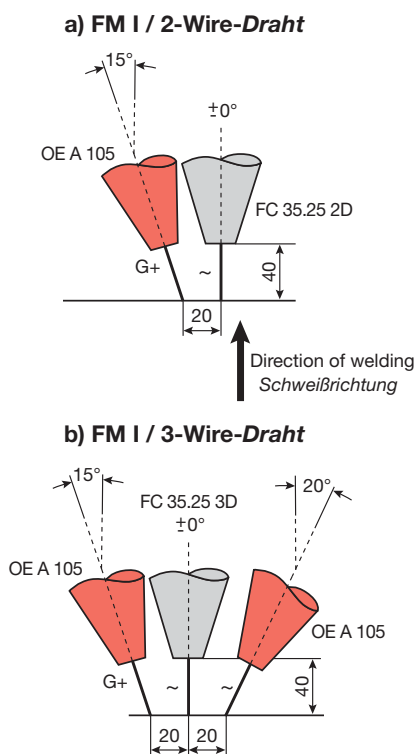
Anordnung der Drahtelektroden und Schweißkopfstellung beim UP-Mehrdrahtschweißen mit dem FMI-Prozess
